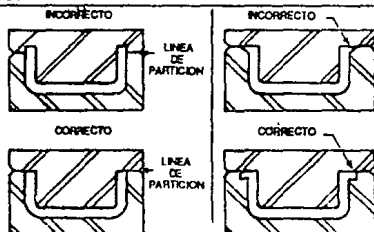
Recomendación para el moldeo de piezas por compresión. (Ref. 2).
